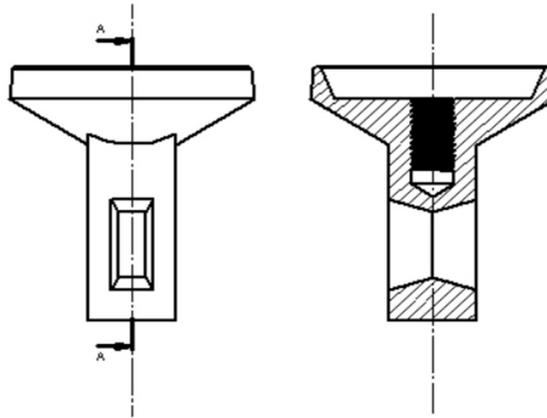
Vista frontal y corte de la pieza que forma parte del obturador del regulador de gas.
